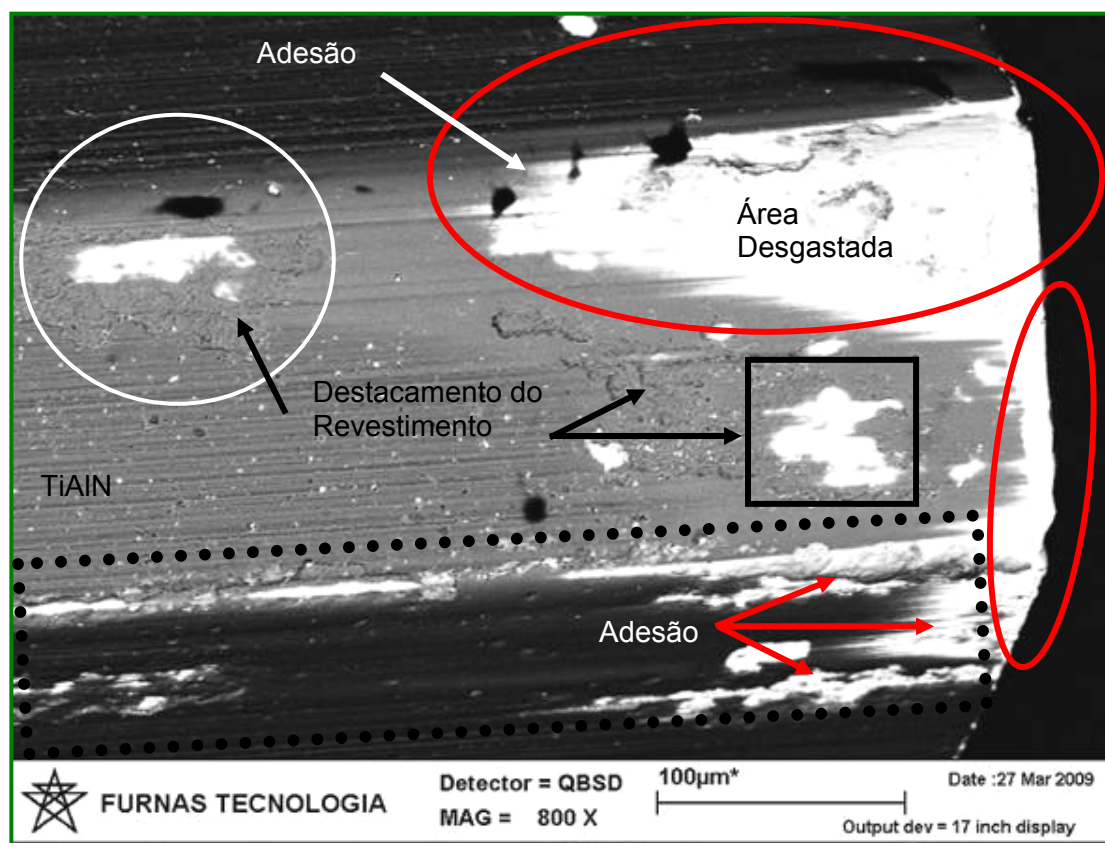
Imagem geral de um dente de um macho de corte que usinou 12.000 roscas
